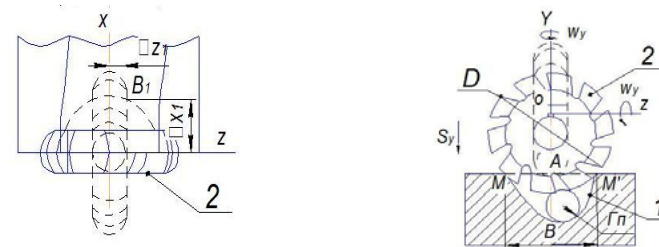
Схема черновой обработки линзообразного участка поверхности детали
